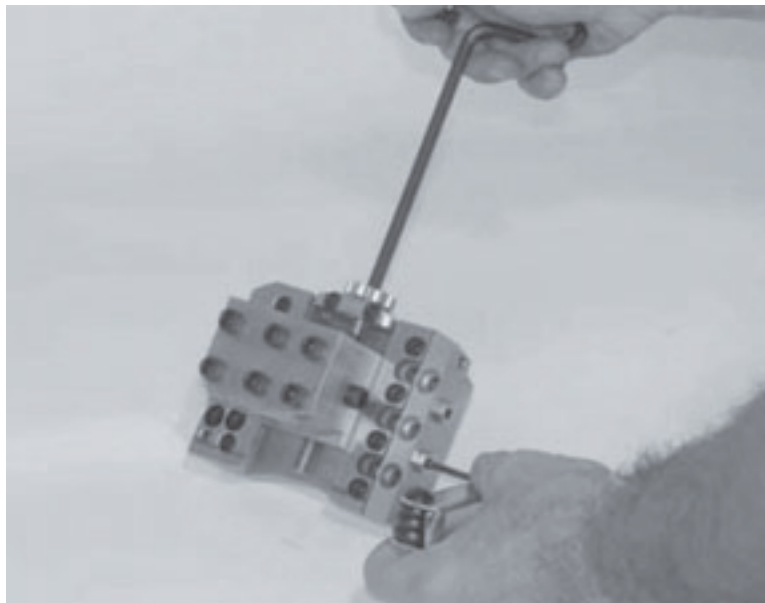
Затягивайте установочные винты, поворачивая звездочку.
